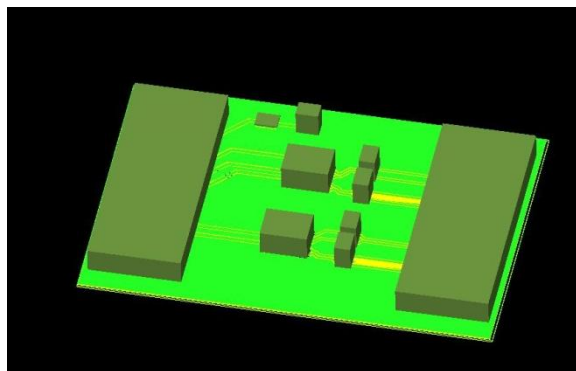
Пример трехмерного изображения печатной платы в системе Cadence Allegro PCB Designer
